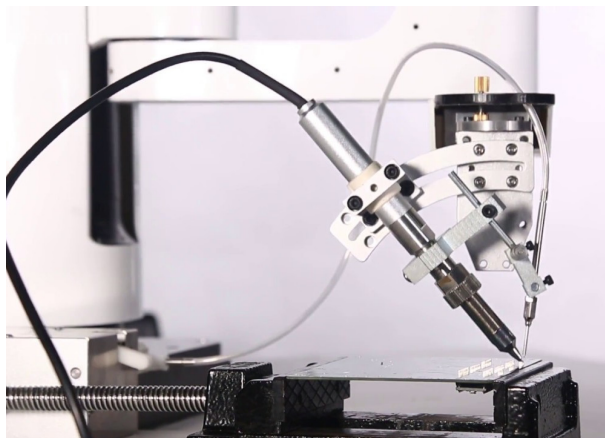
Robot Dobot M1 realizando una soldadura con estaño
